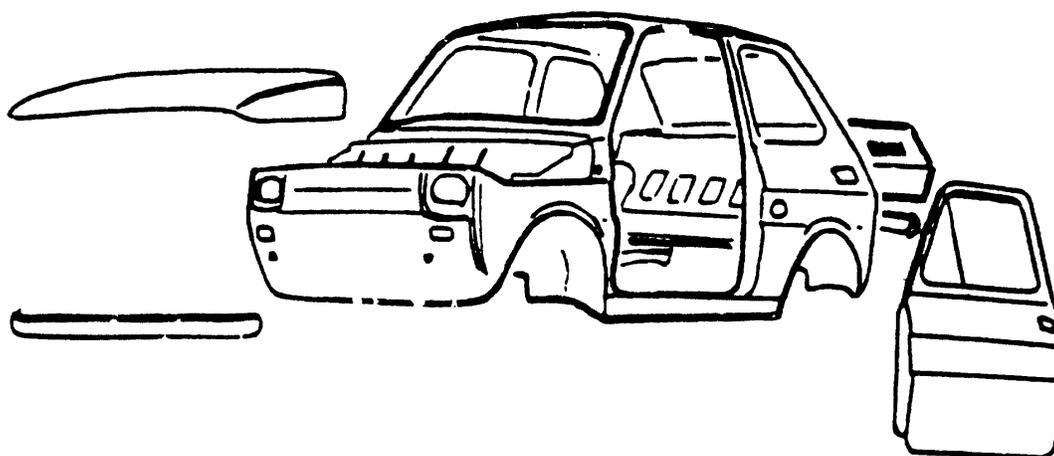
Carrocería monocasco, unida por soldadura.⁸
